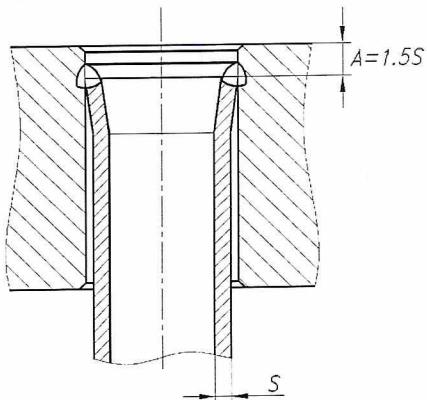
Труба, заглубленная в отверстие трубной решетки
